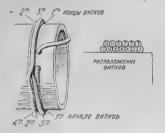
Способ намотки и расположение витков двуслойной катушки.
